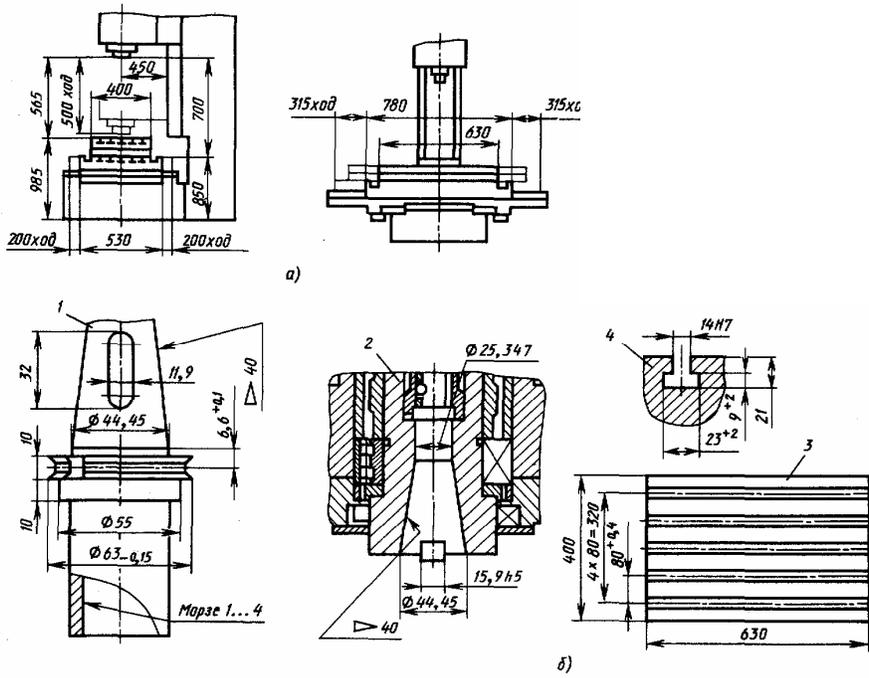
Габариты рабочего пространства (а) и установочные базы (б) вертикального сверлильно-фрезерного станка мод. 21104П7Ф4 (1 – оправка; 2 – шпиндель; 3 – стол; 4 – средний паз стола)
